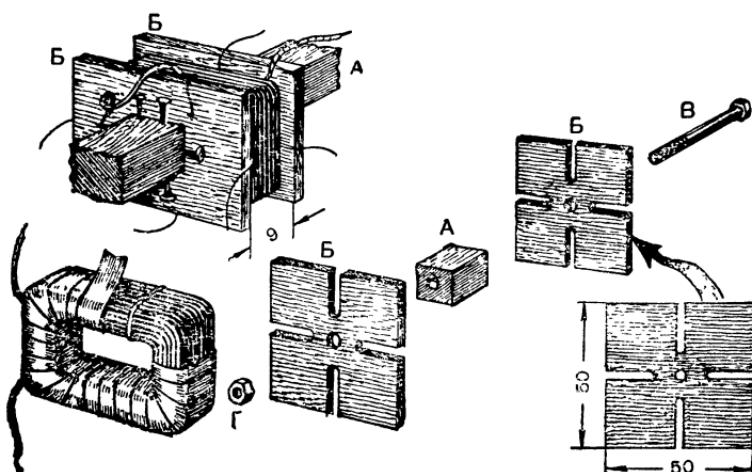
Приспособления для намотки катушек статора: слева — простейшее приспособление, внизу — готовая катушка, справа — более совершенное приспособление; А — болванка; Б — щечки; В — болт; Г — гайка.
